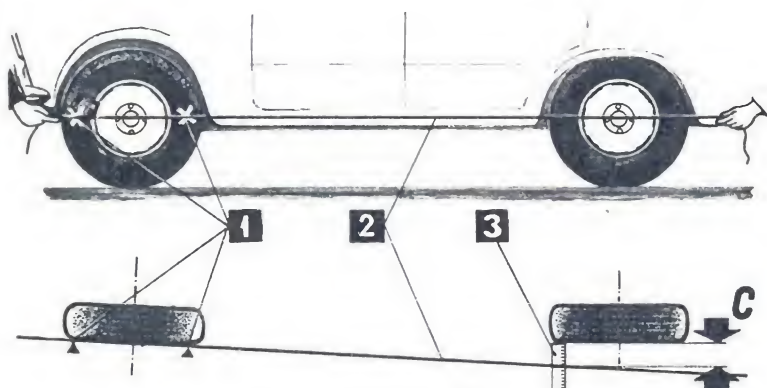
Определение схождения колес: 1 — точки равного биения; 2 — шнур; 3 — линейка; с — расстояние от шнура до передней части боковины покрышки заднего колеса.
